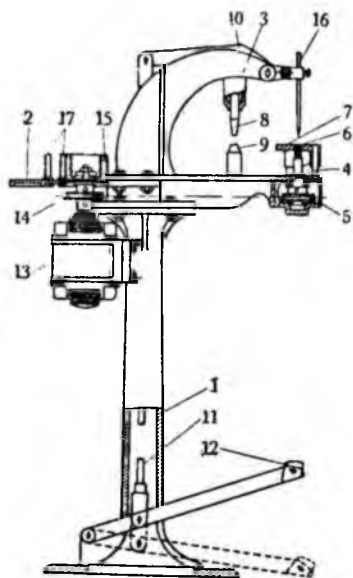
Общий вид станка для переделки и зачистки ферродо:
